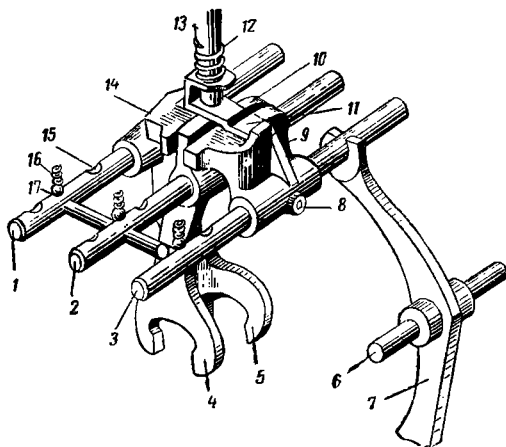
Механизм переключения передач четырехступенчатой коробки передач автомобиля ГАЗ-51.
